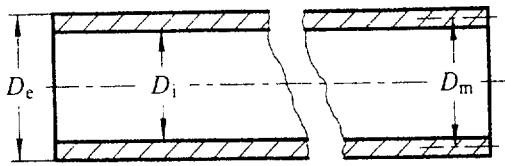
Tuyau sans soudure
